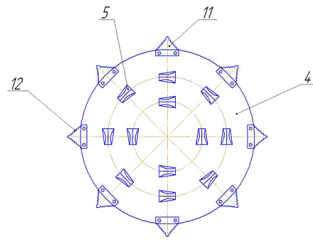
Конусообразный рабочий орган измельчителя кормов
